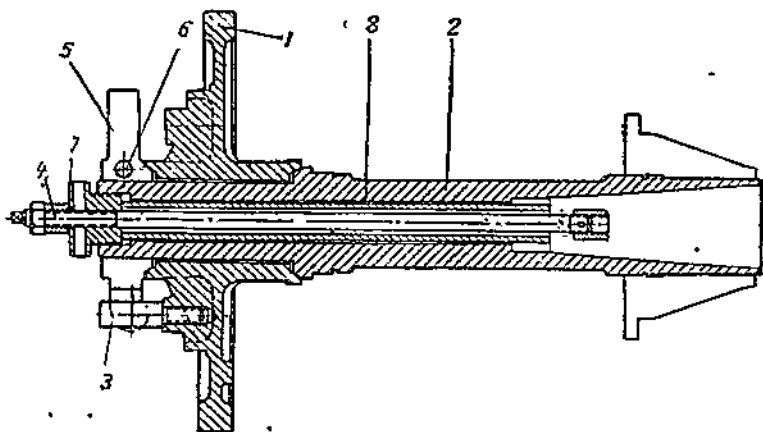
Механизм деления зубошлифовального станка Оркутт.
